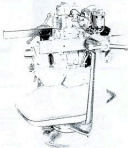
Motore montato sul quadrante rotabile, per la revisione.
